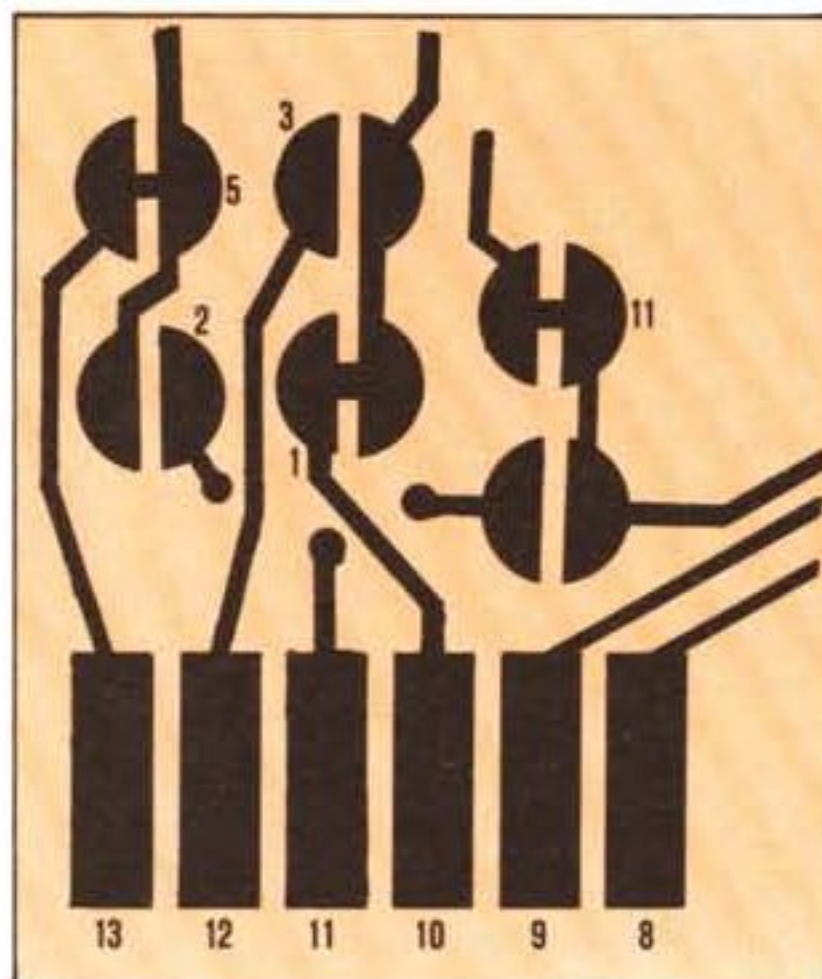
Particolare della espansione 3K RAM prima di correggere i pallini.
